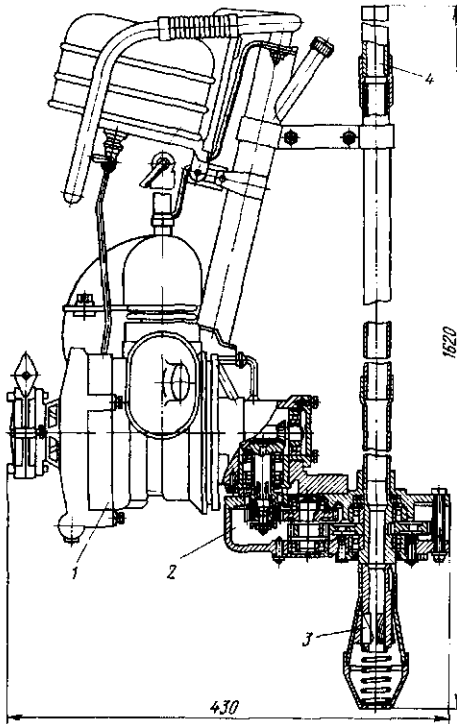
Приспособление ПЗД-12 для свертывания электродов заземления
